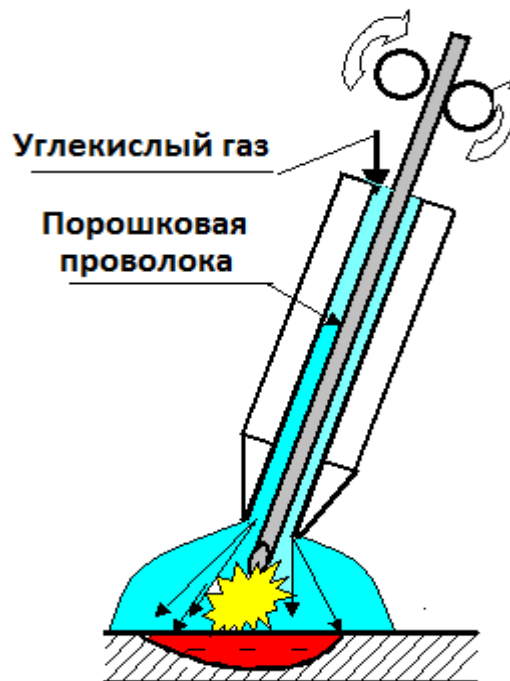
Схема сварки порошковой проволокой с дополнительной защитой сварочной ванны углекислым газом
